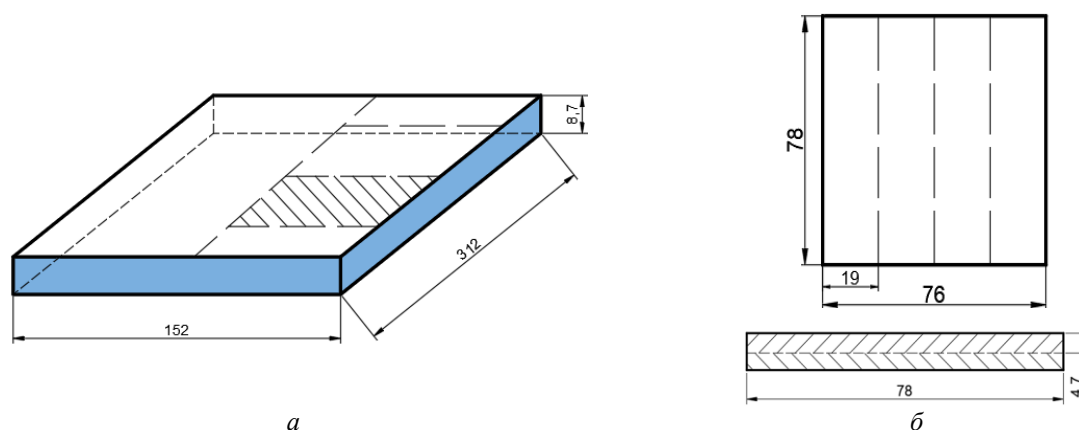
Схема вырезки образца из сваренного КМ (а) и подготовка образцов для прокатки (б)
